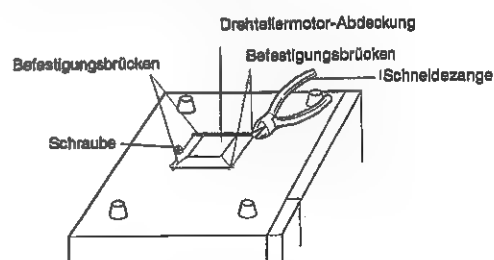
(a). Ausbau der Drehtellermotor-Abdeckung
